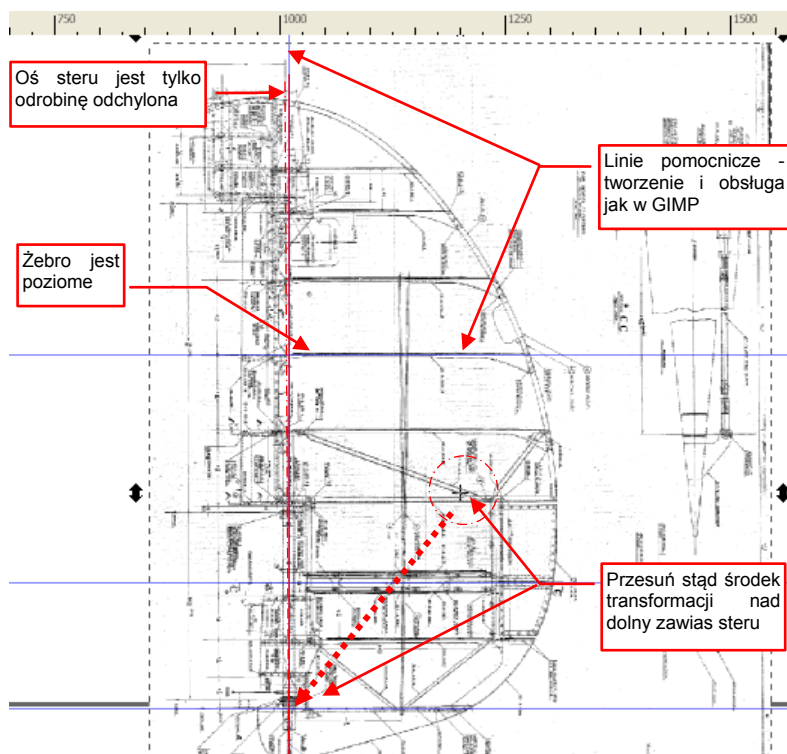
Wstępne przygotowanie rysunku
